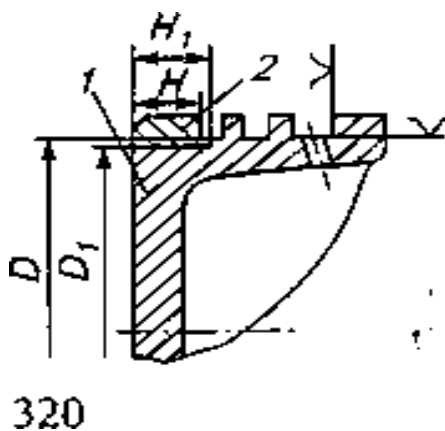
Схема установки додаткової ремонтної деталі при відновленні канавки під поршневі кільця:
